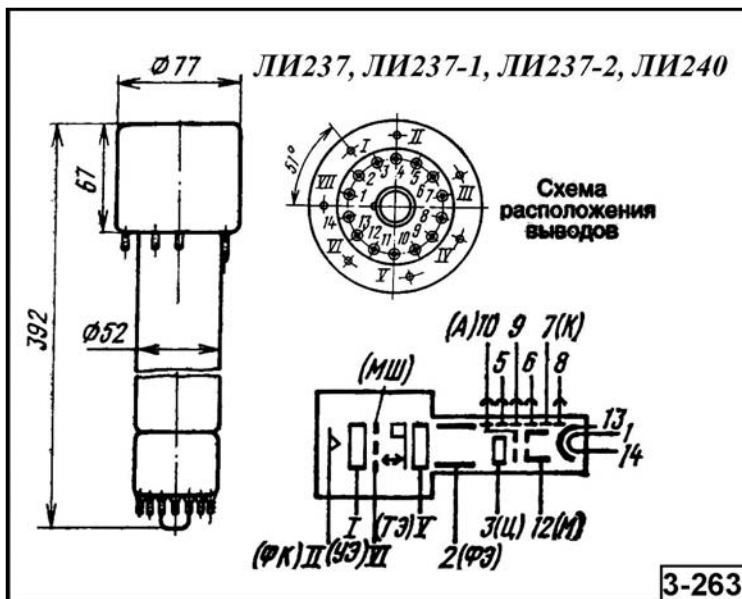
Внешний вид, габаритные размеры и назначение выводов суперортиконов
